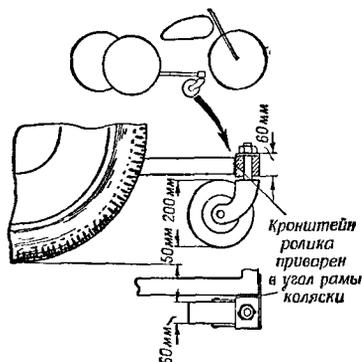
Установка ролика на раме коляски для страховки от опрокидывания мотоцикла с высокой пирамидой
